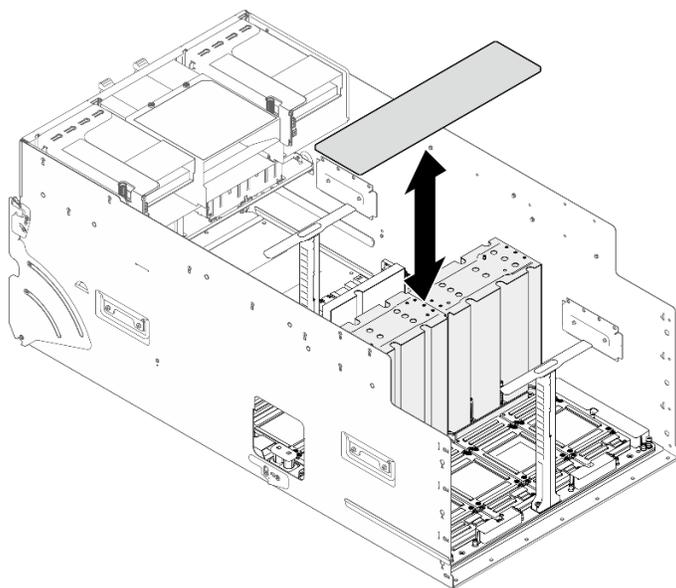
Remoção da tampa do dissipador de calor NVSwitch
